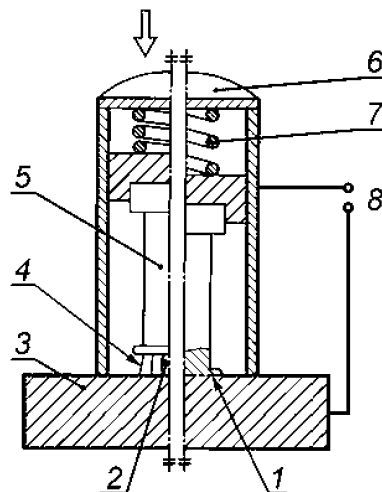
Приварка дуговая шпилек конденсаторная растягиваемой дугой
